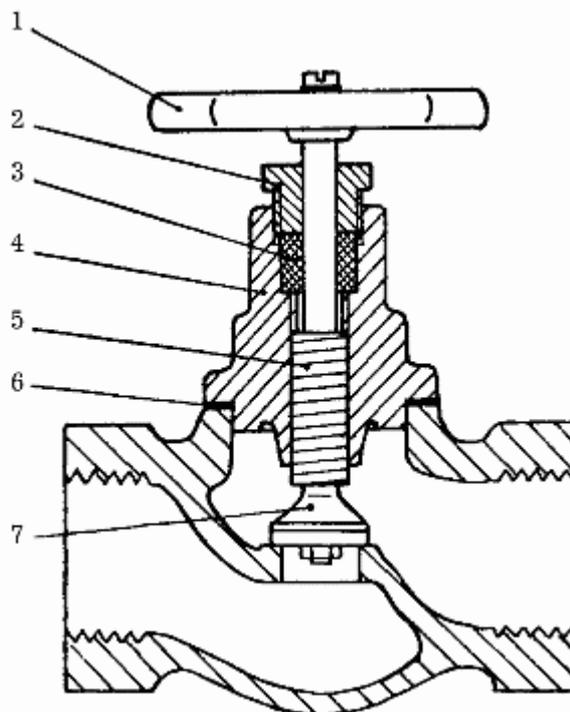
Устройство вентиля: 1 – маховик; 2 – втулка; 3 – набивка сальника; 4 – корпус головки; 5 – резьба штока; 6 – изоляция; 7 – клапан с прокладкой.
